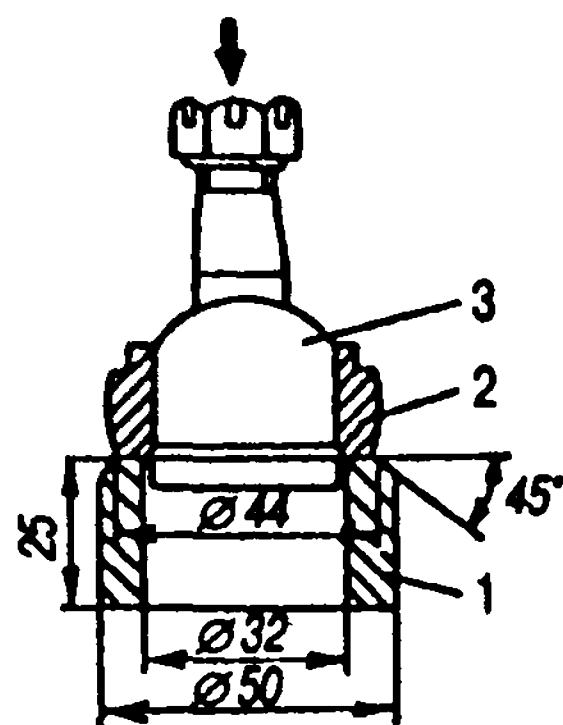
Выпрессовка шарового шарнира: 1 - втулка; 2 - наконечник; 3 - шаровой шарнир
